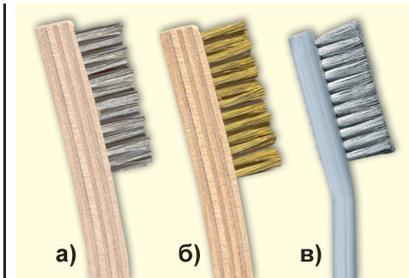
Абразивные щетки: из нержавеющей стали (а); из латуни (б); из нержавеющей стали с алюминиевой ручкой (в)
